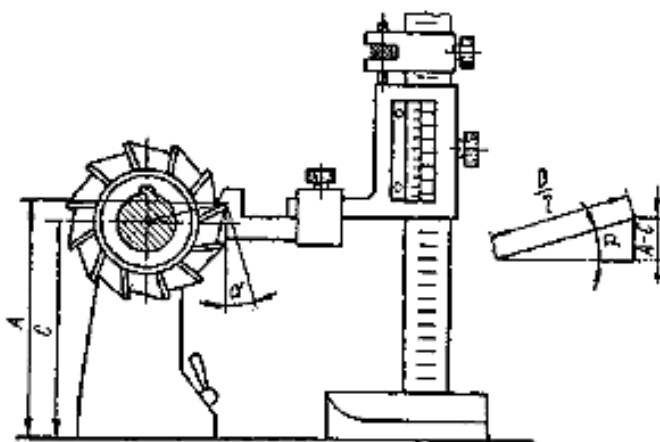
Контроль заднего угла фрезы штангенрейсмасом
